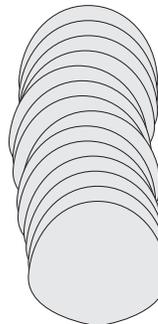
Излишнее перекрытие сварочных ванн
